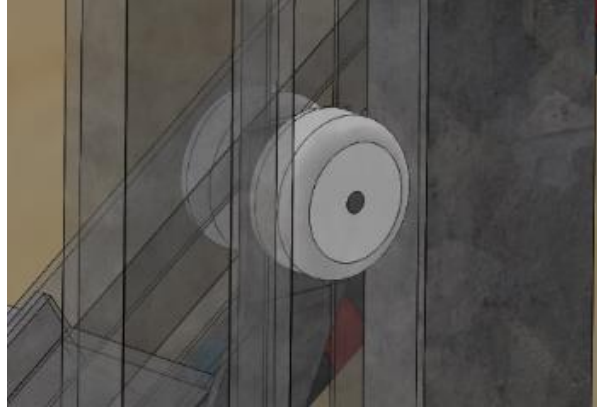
Kaldırma platformu destek profilleri SW çizimi.
